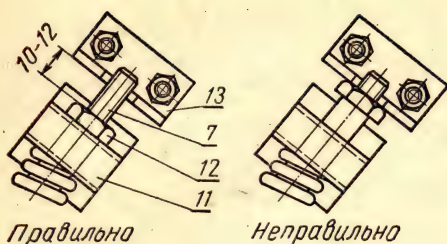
Положение центрирующей втулки устройства по регулировке натяжения плавающего транспортера (обозначения см. в подписи под рис. 33).
